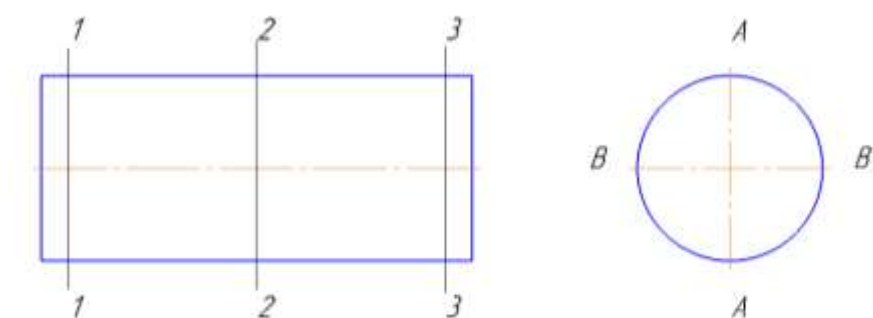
Схема контроля гладкой цилиндрической поверхности
